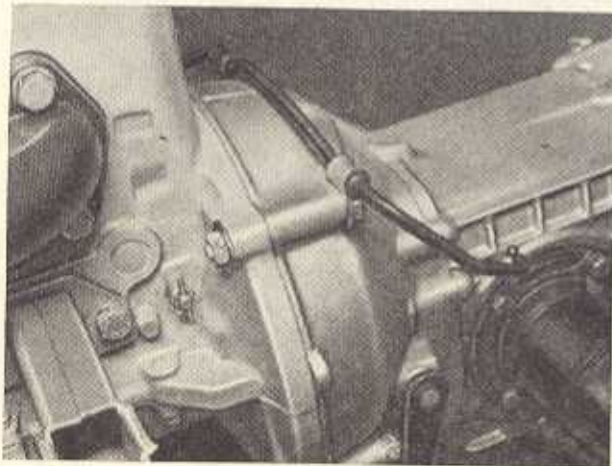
Lagerung der Gestängewelle beim Baumuster 353
